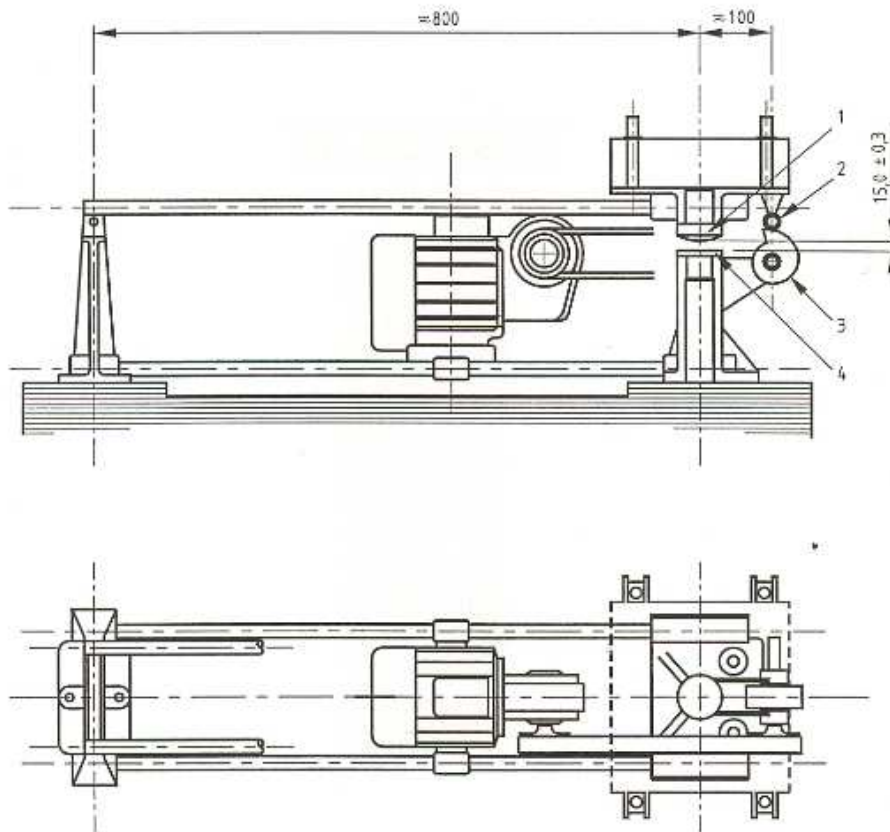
Esquema com dimensões do compactador (dimensões em milímetros) [40].
